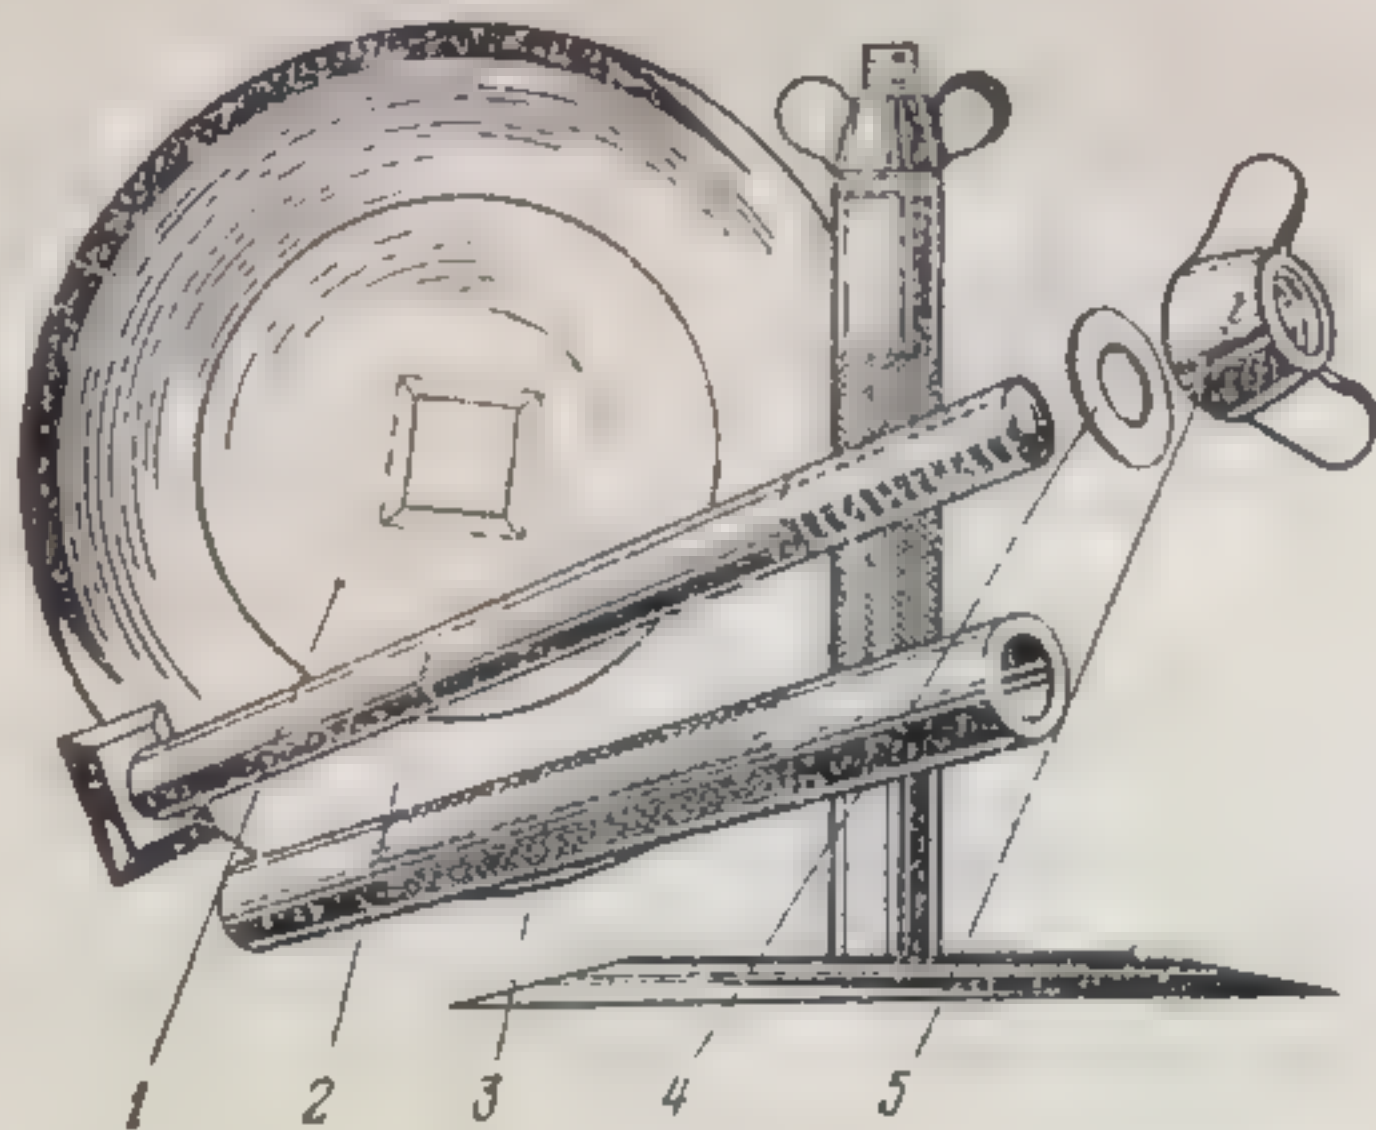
Дисковый нож: 1 — режущий диск; 2 — стержень — основание; 3 — рукоятка; 4 — шайба; 5 — гайка
